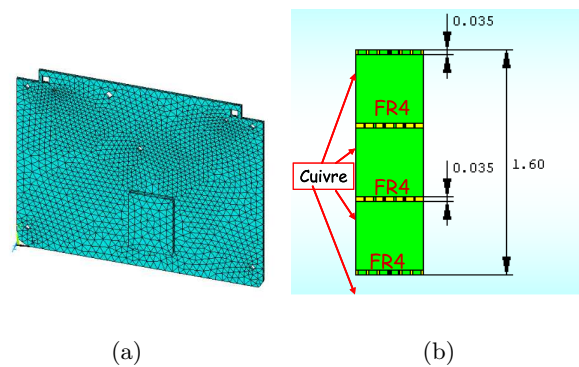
(a) Maillage EF du PCB et du composant principal (b) Coupe transversale du PCB
